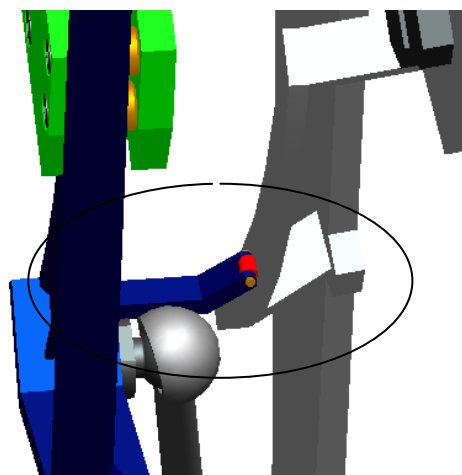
Detail zamezení vertikálního
